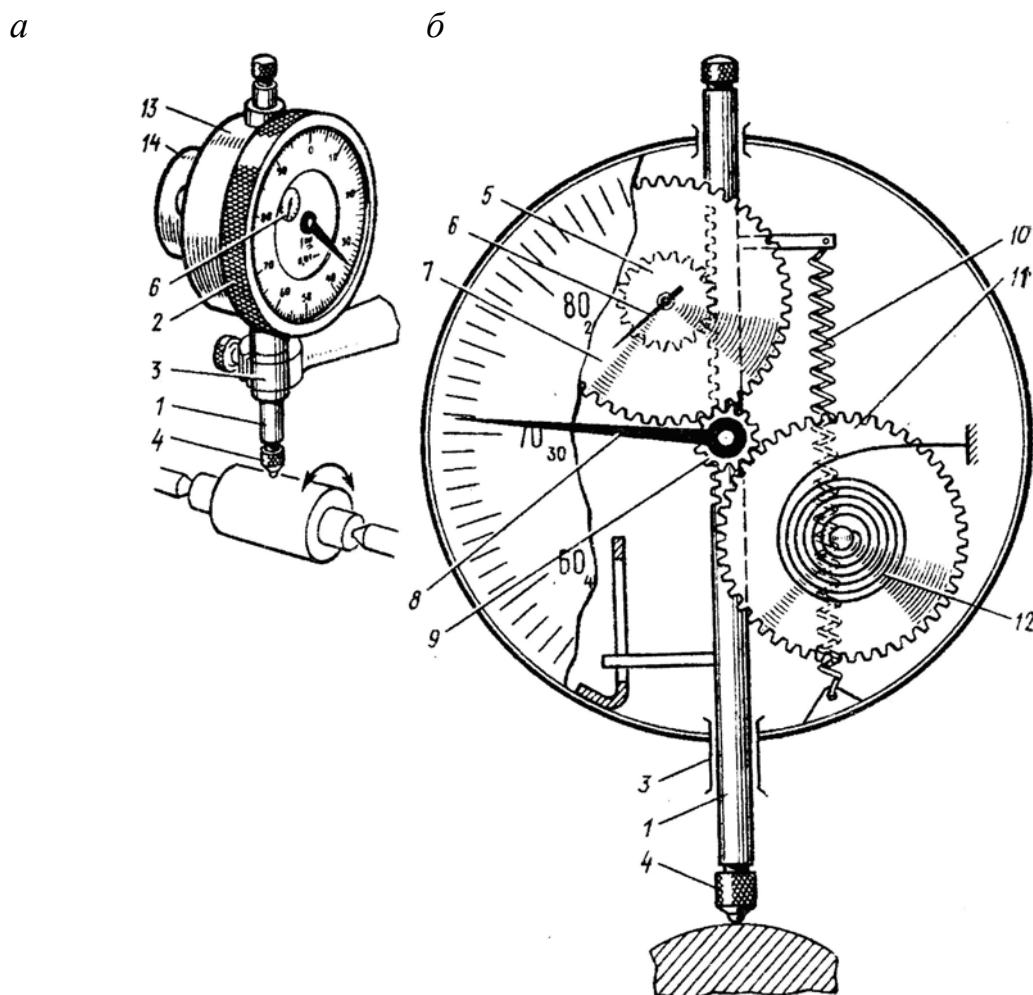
Индикатор часового типа: а - общий вид; б - схема зубчатой передачи
